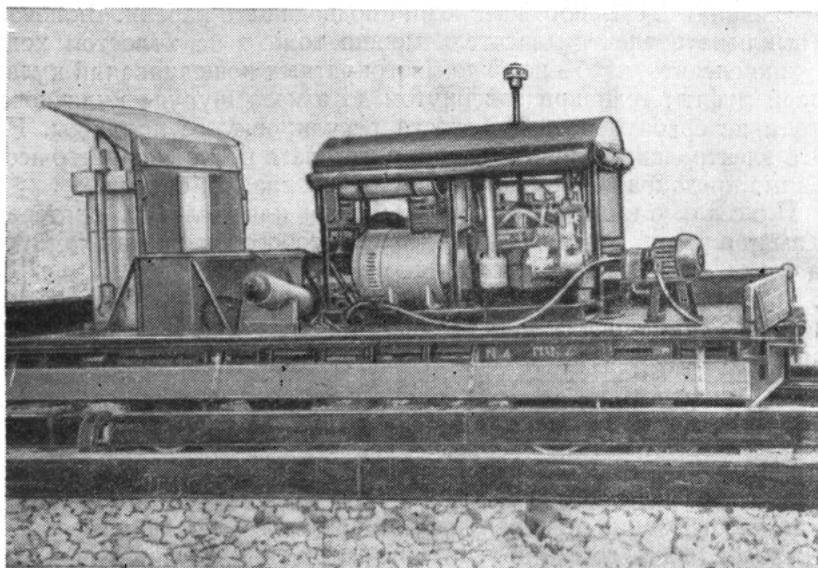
Общий вид передвижного сварочного агрегата САК-2
